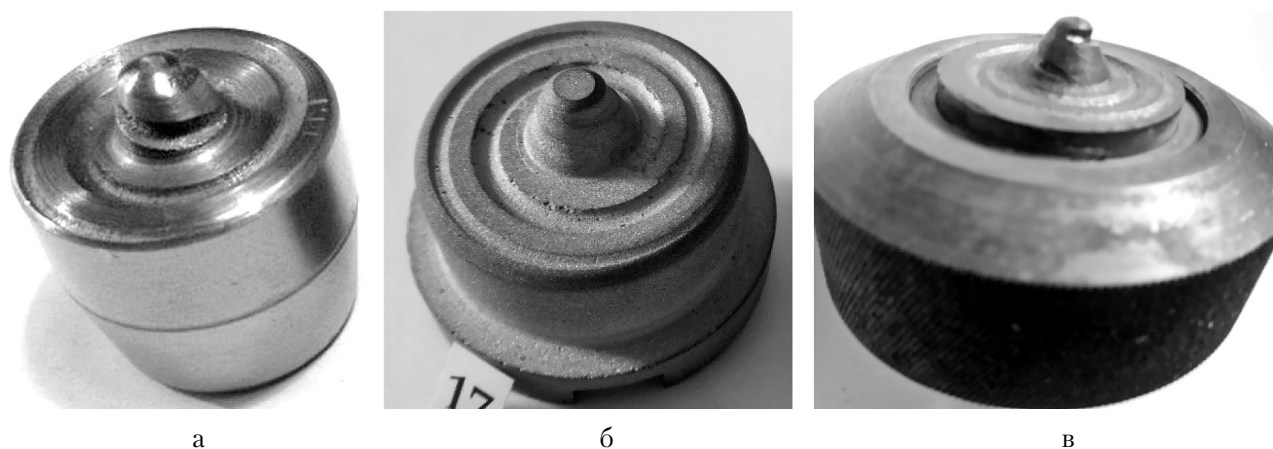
Общий вид инструментов для сварки, наплавки и модификации металлов трением с перемешиванием [4–6]: а – из стали P18, для СТП алюминиевых и магниевых сплавов; б – из твердого сплава ВК8 для наплавки и точечной клепки; в – из кубического нитрида бора (Кубонит) для наплавки никеля и кобальта
